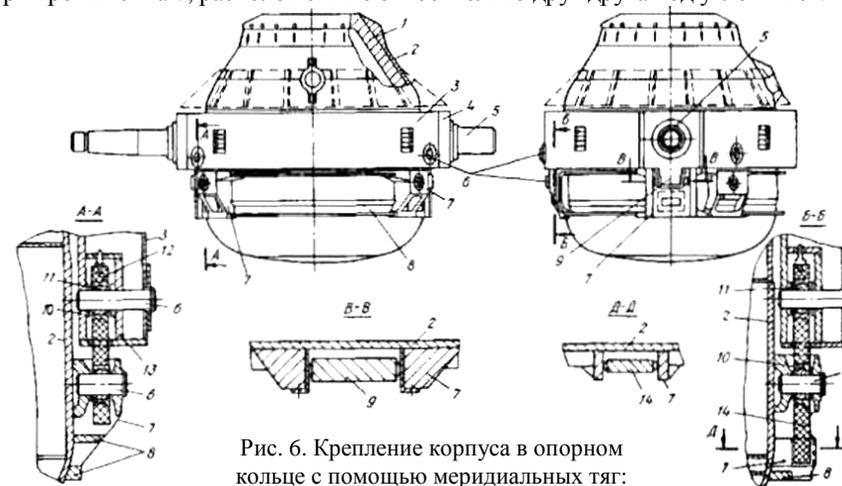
Крепление корпуса в опорном кольце с помощью меридиальных тяг:
